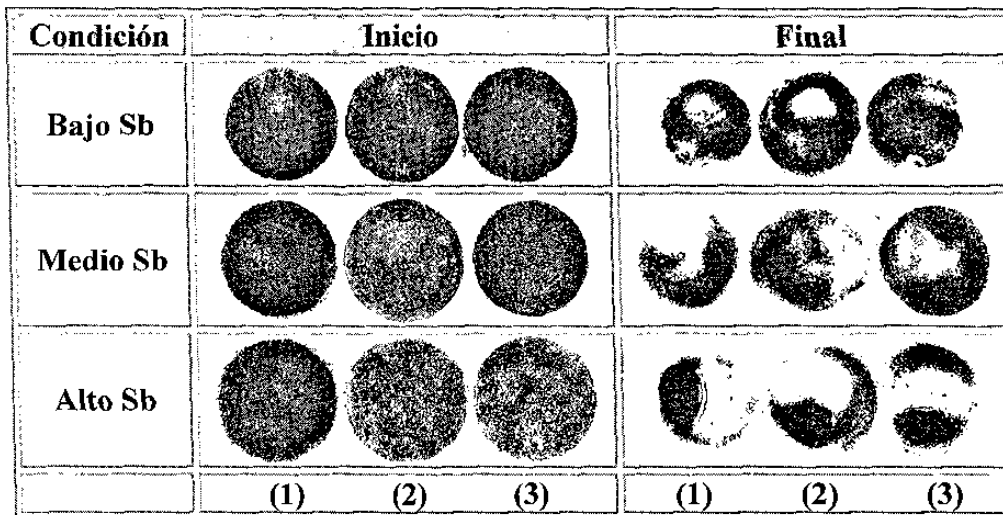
Impresión de la huella del electrodo al inicio y final de la prueba de soldadura, (1) compuesta, (2) electrodo superior y (3) electrodo inferior.
